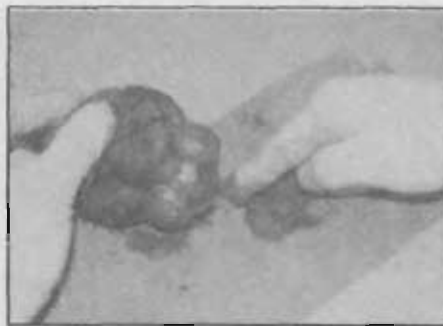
Очистка трипоидного шарнира от смазочного материала
